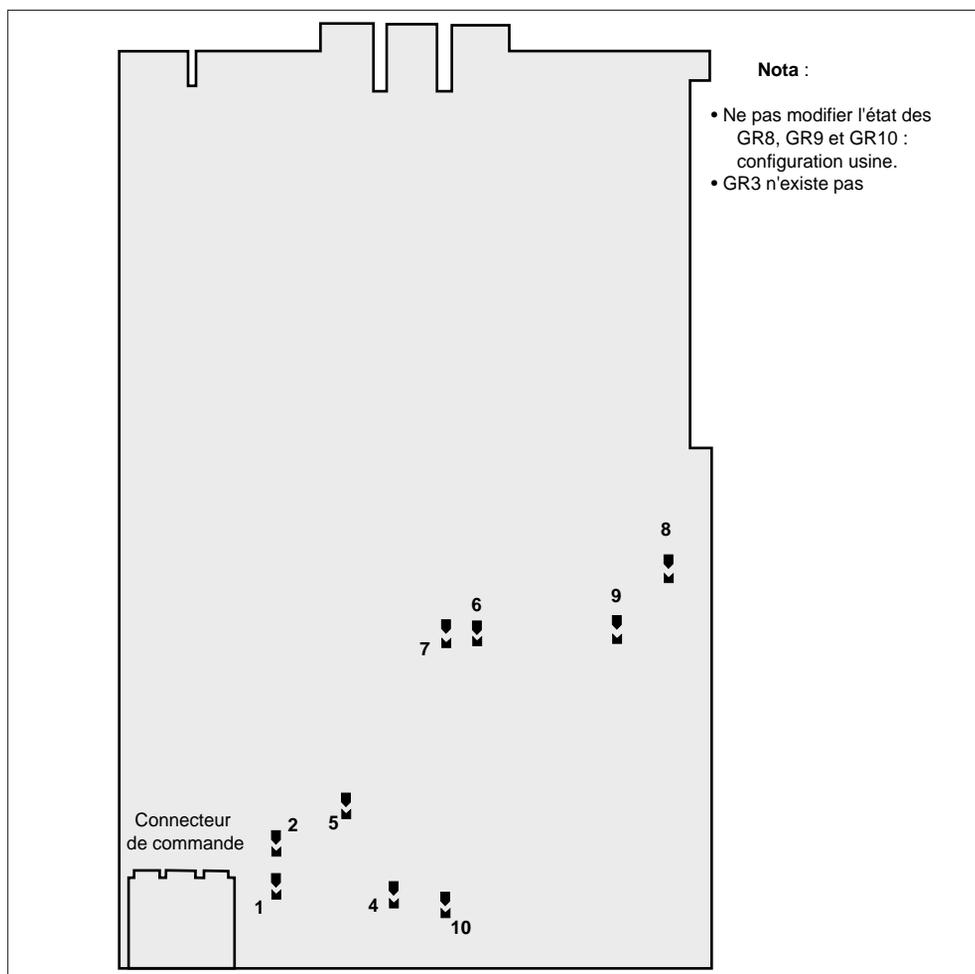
Emplacement des «grains de café» (GR) de configuration (vue côté soudures)
